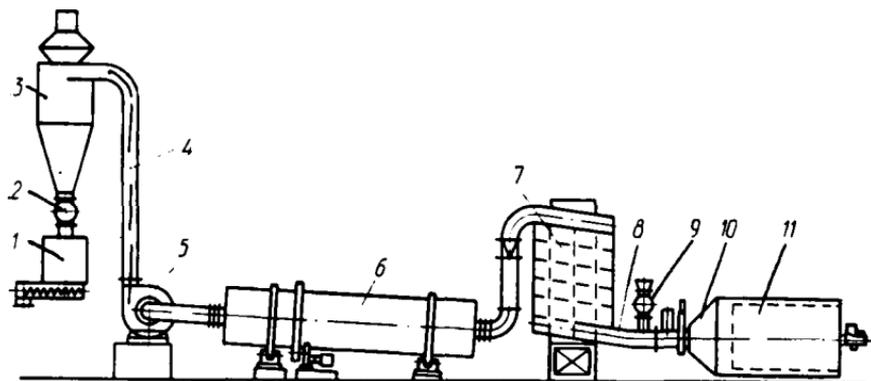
Схема агрегата комбинированной сушки стружки АКС-5:
